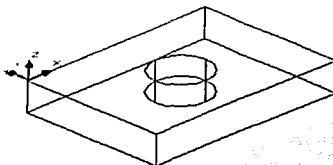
Placa retensora con un corte circular en la parte central.
